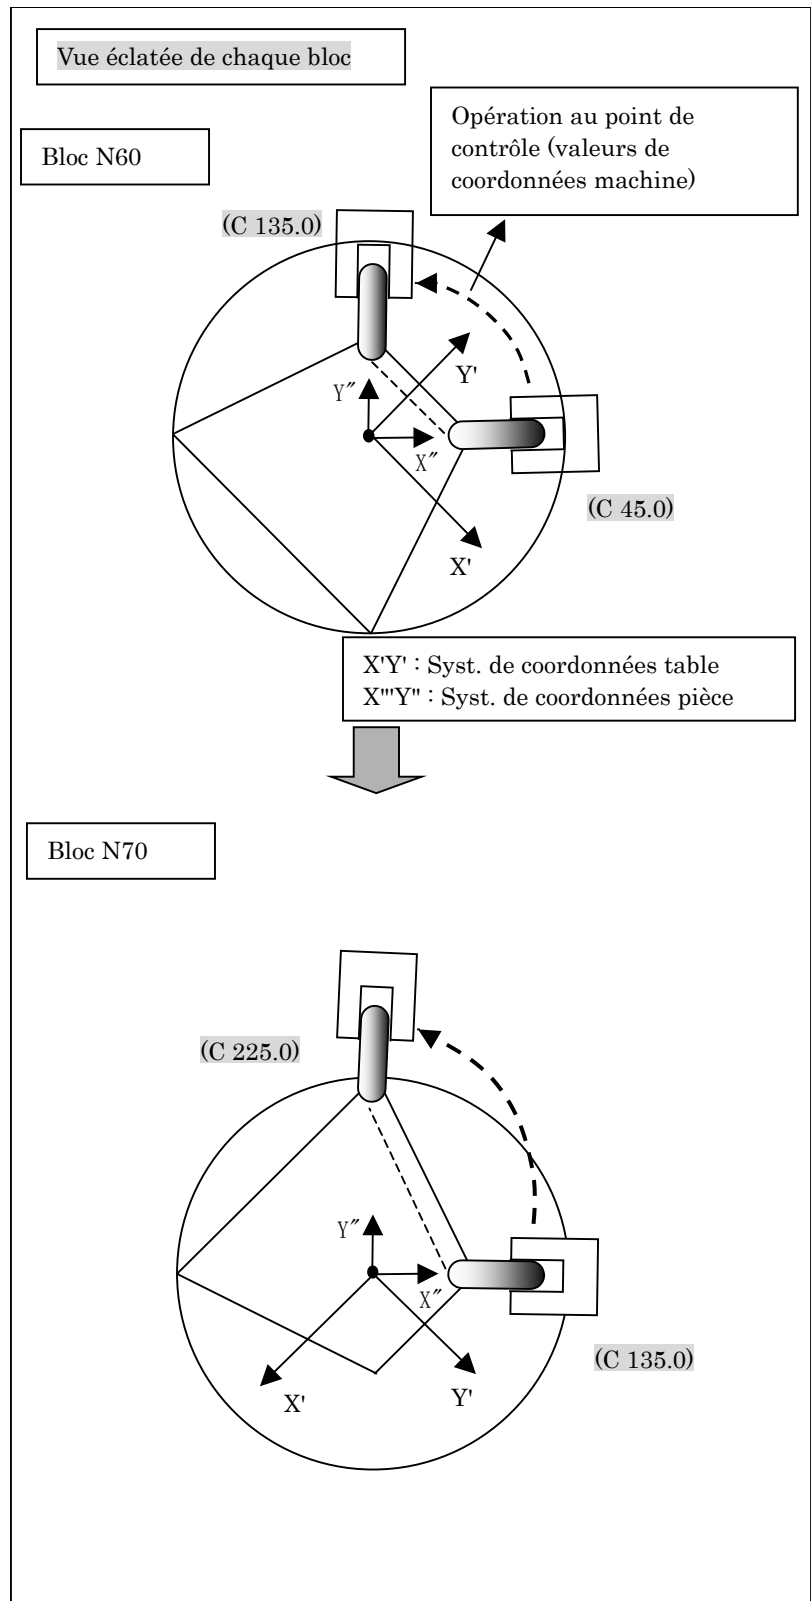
(c) Vue éclatée de chaque bloc (1)
